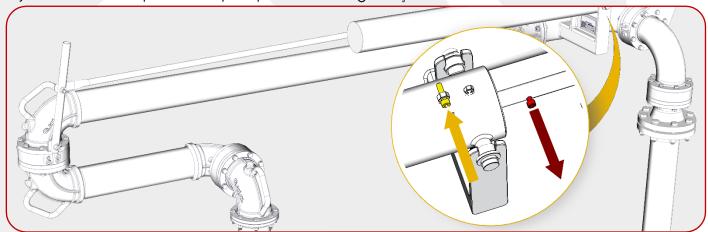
Retirar o Parafuso de Trava do Conjunto de Mola
